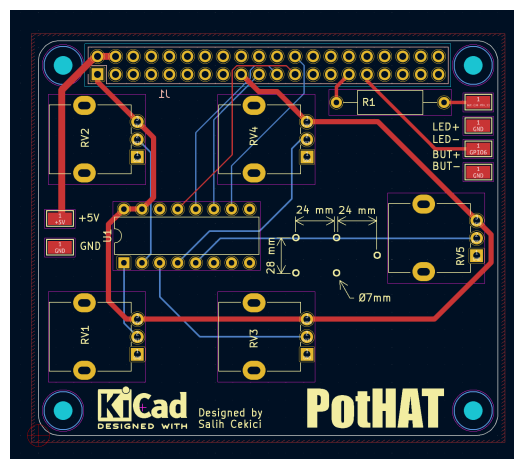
PCB Layout des PotHATs in Kicad
